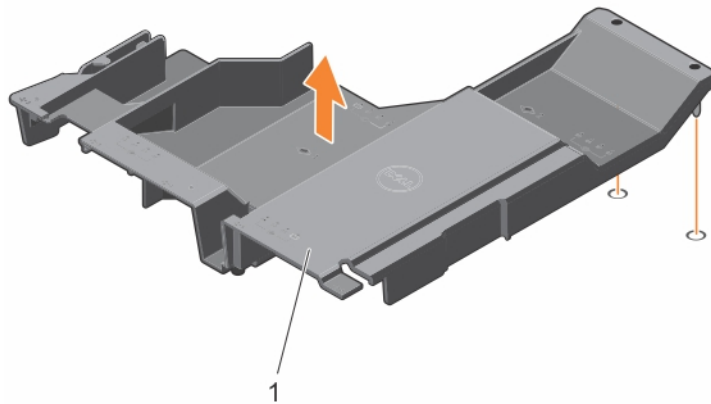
Extracción de la cubierta de refrigeración (procesador de 135 W)
